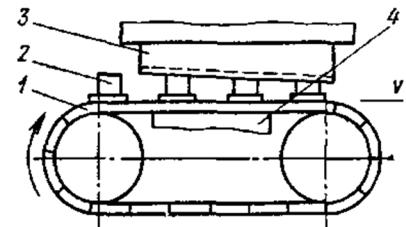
Схема обработки заготовок на протяжном станке непрерывной обработки
